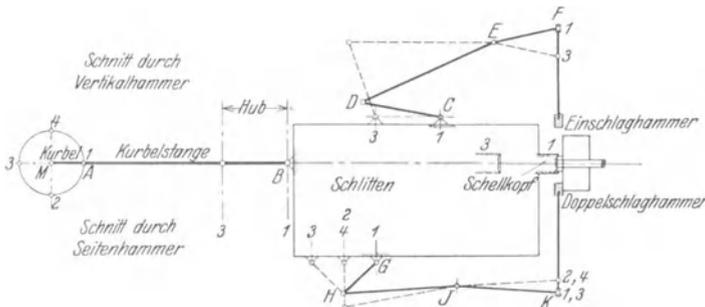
Schema der Bolzenkopfschmiedemaschine.
